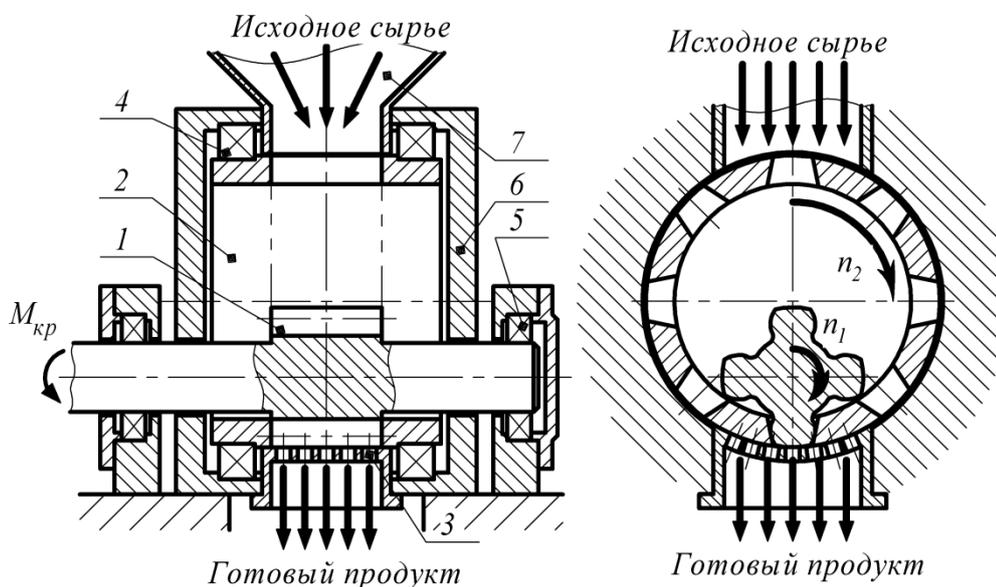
Схема измельчителя с зубчатой передачей внутреннего зацепления
